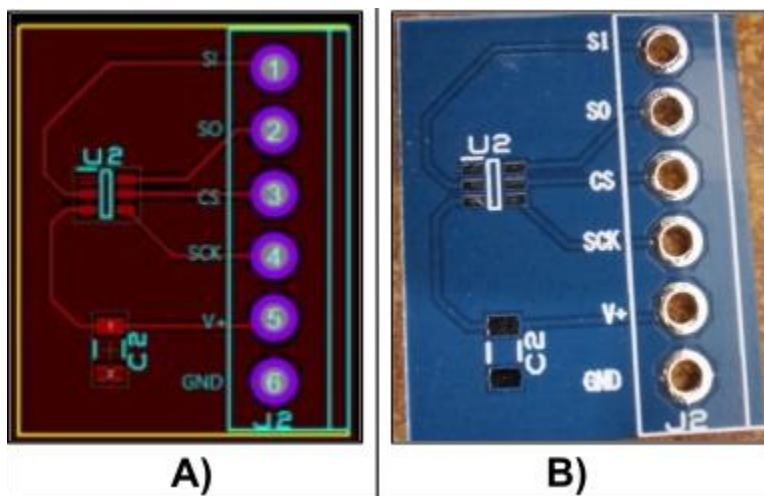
A) Diseño en PROTEUS del sensor digital y B) PCB del TM125.
